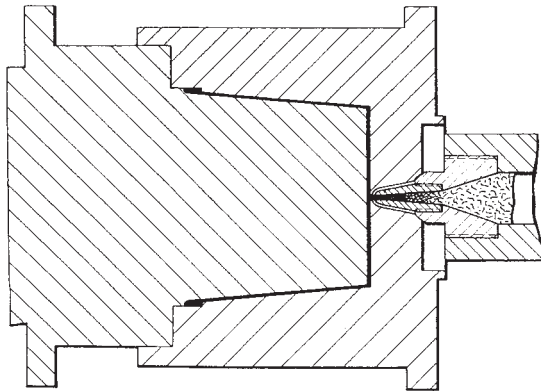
Einfachste Ausführung eines Isolierkanalsystems (nach [12])
